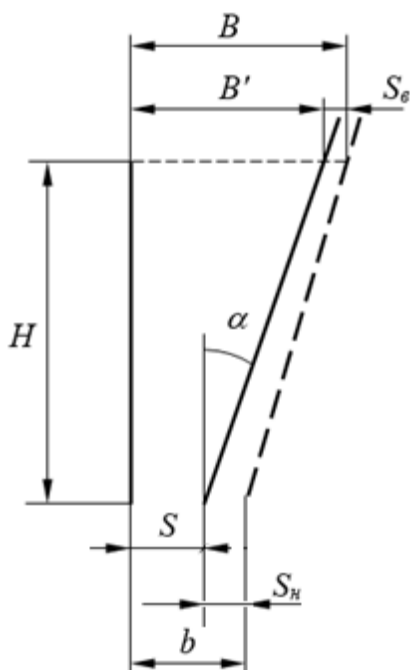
Схема геометричних розмірів щокової дробарки
